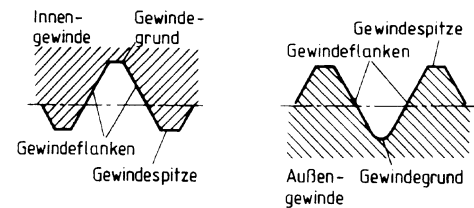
Gewindeflanke, Gewindespitze, Gewindegrund
